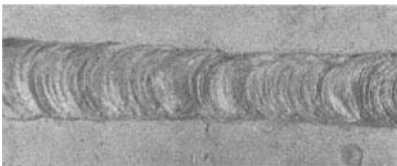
Mit dem Metalllichtbogen geschweißte Aluminiumnaht.
